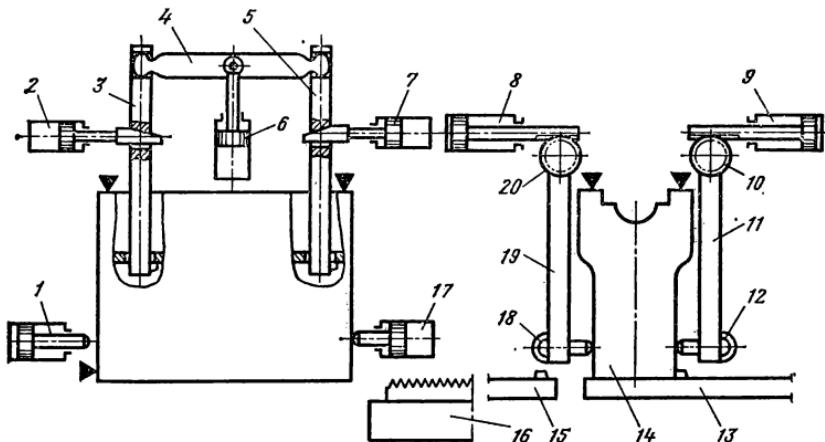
Схема приспособления протяжного станка ЛМ-1-С6:
